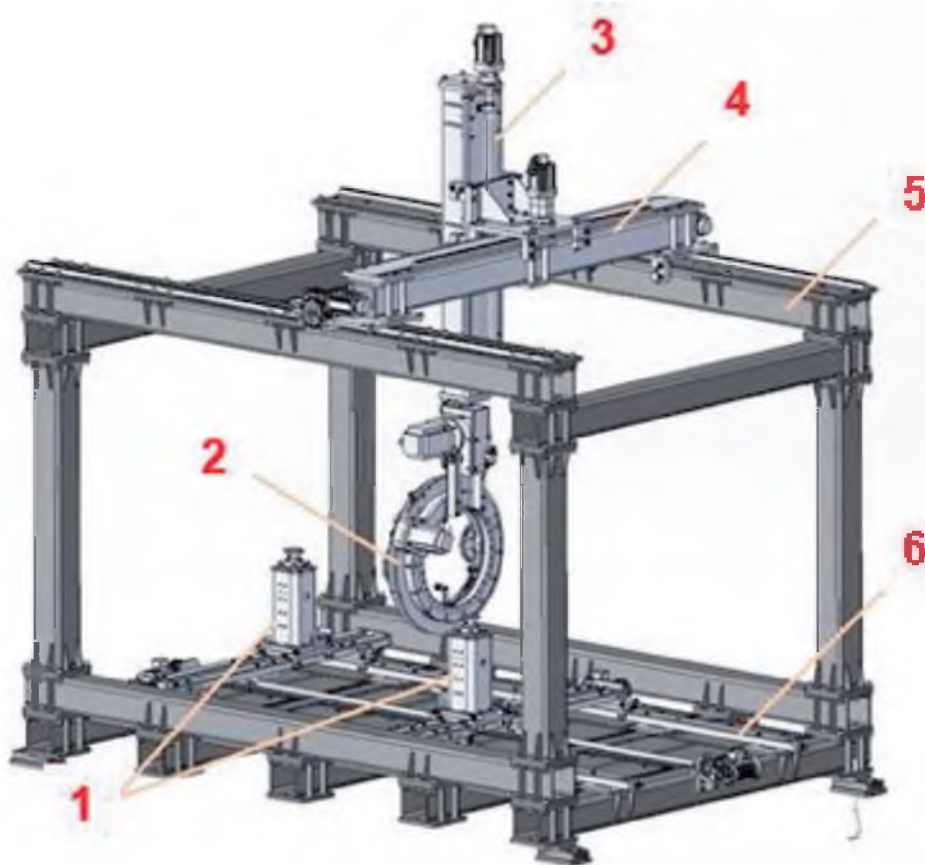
3D-компоновка станка СМП-33М: 1 – механизм подъёма оправки; 2 – вертлюг; 3 – ползун; 4 – траверса; 5 – станина; 6 – механизм перемещения оправки
